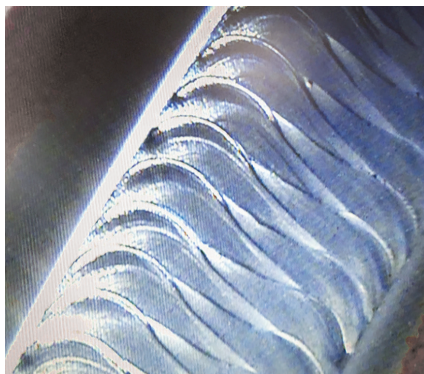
Вид облицовочного шва при ВИГ-сварке с подогретой проволокой толстостенных соединений "труба-отвод"
